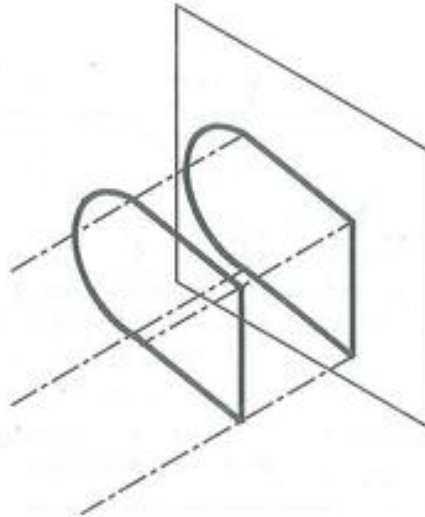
Proyección de una superficie paralela al plano de proyección.
